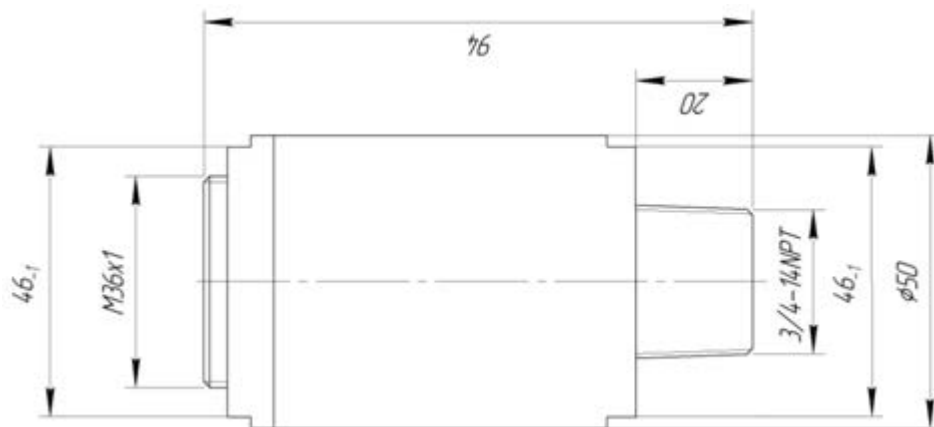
Габаритные размеры преобразователя газового универсального
